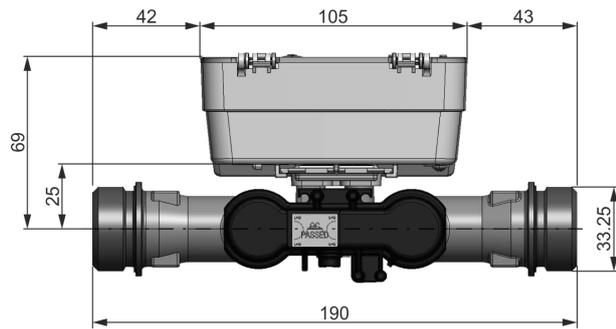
Abb. 5: Übersicht Masse Baulänge 190 mm (Gewinde)
